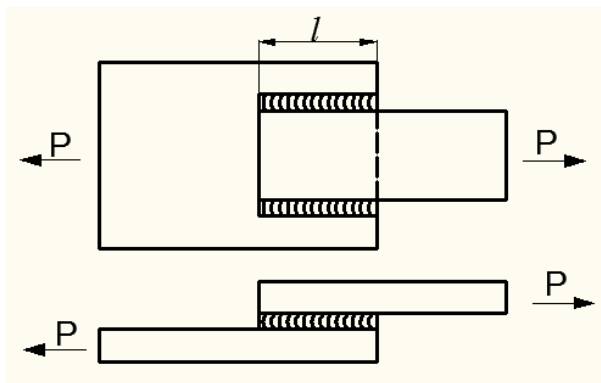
Розрахункова схема напусткового зварного з'єднання з фланговими швами
